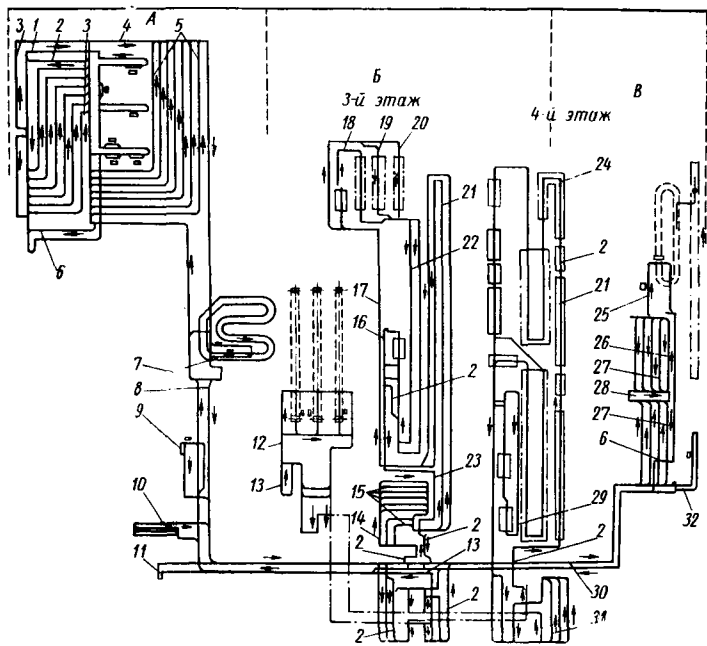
Транспортная система, связывающая прессовый корпус А, кузовной цех Б и главный конвейер сборки автомобилей В:
